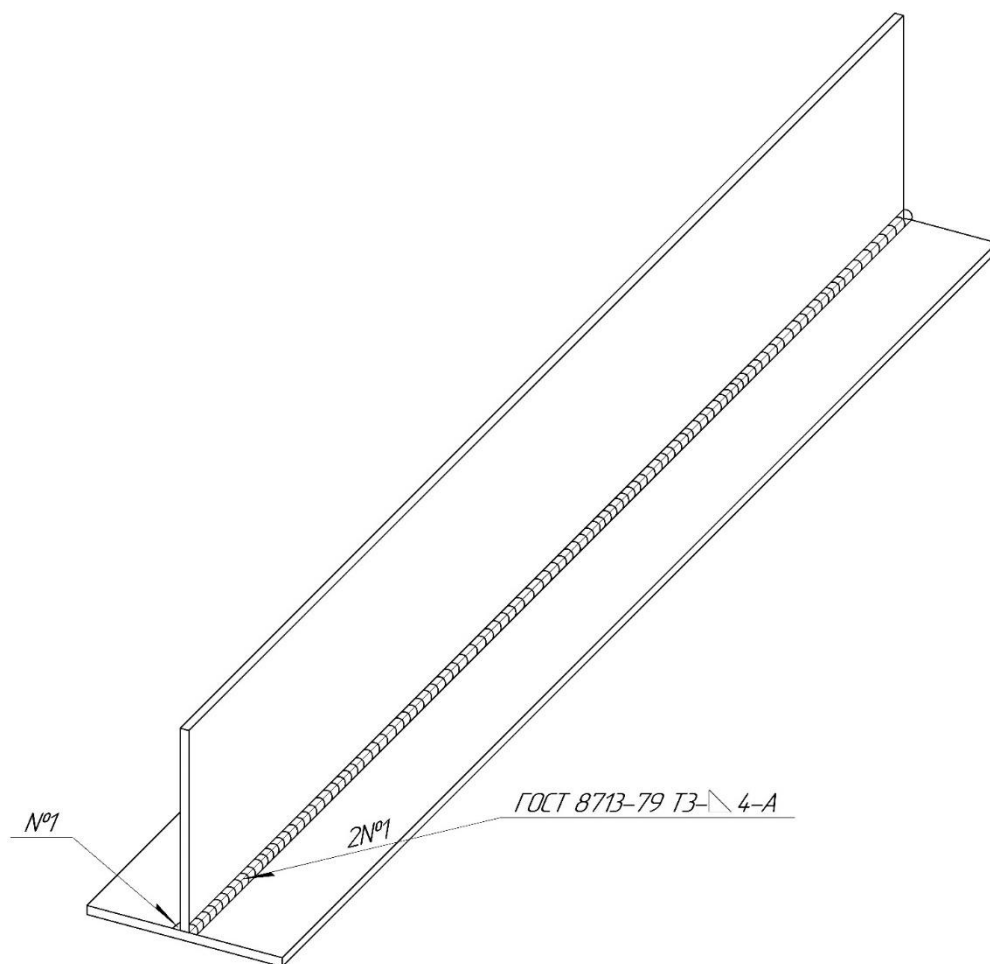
Итоговый чертёж изготовленной сварной конструкции
